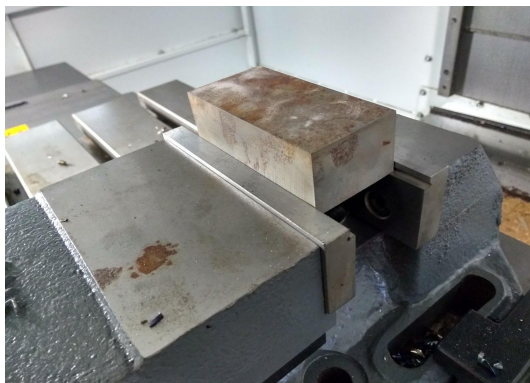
Fixação do corpo de prova para usinagem (Autoria própria).
